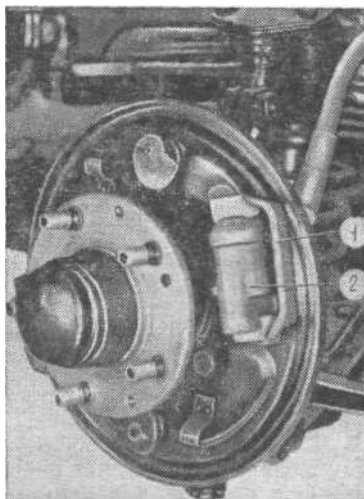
Закрепление поршней колесного тормозного цилиндра автомобиля модели 407 при помощи скобы:
